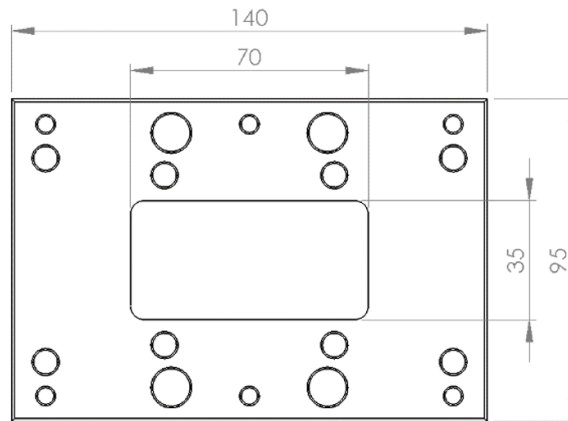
Vista de planta de la placa aïllant (Font pròpia)
